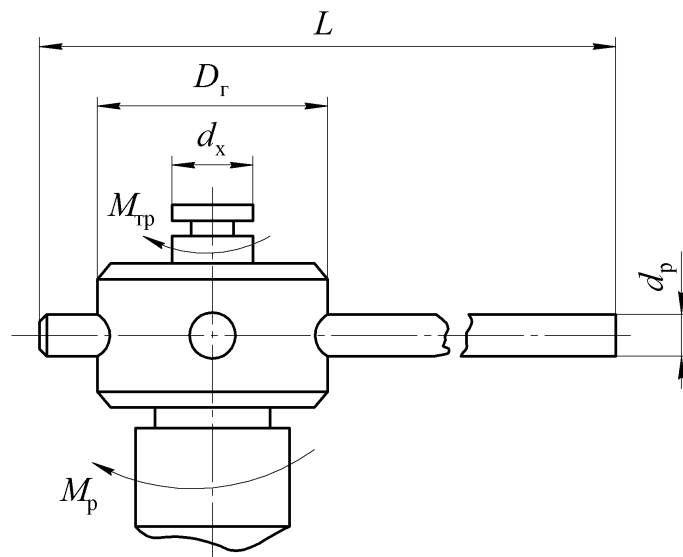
Розрахункова схема для головки і рукоятки вантажного гвинта.
